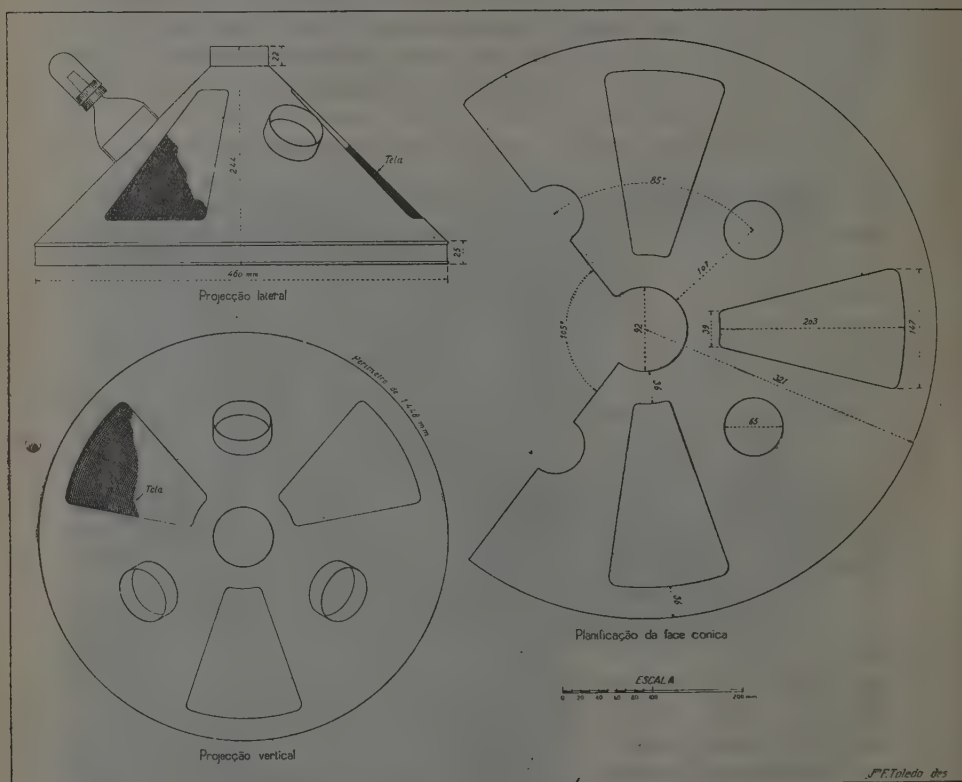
Aparelho armadilha para apanhar "Vespas de Uganda". Detalhe da construção do aparelho da figura 21.
